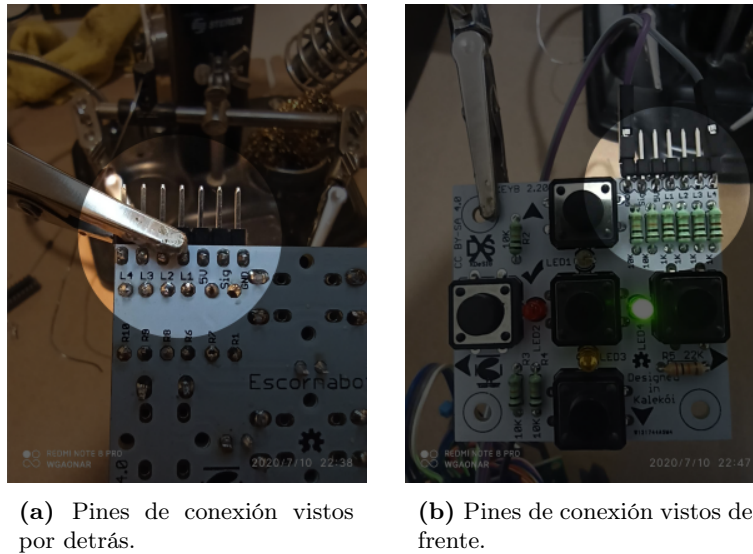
Soldadura de los pines de conexión en la botonera.
